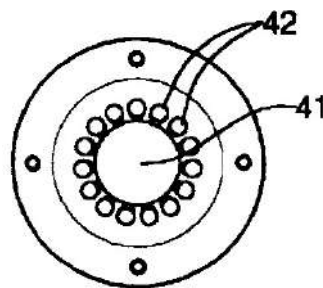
Пристрій і його вид з торця на циліндричну форсунку
